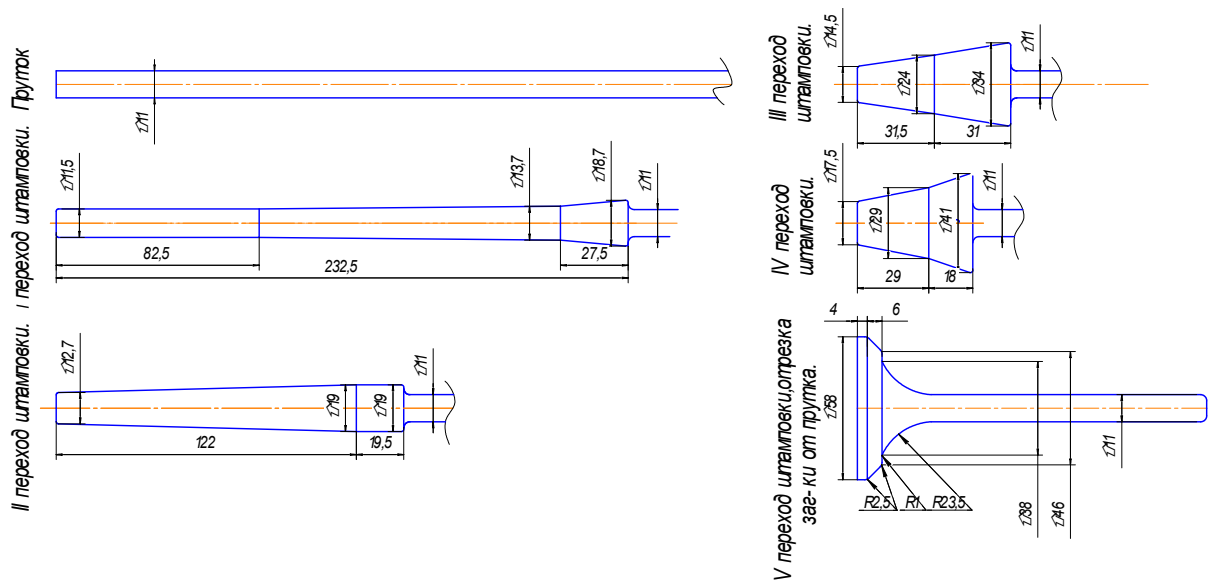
Штамповка заготовки на ГКМ за пять переходов, с последующей отрезкой заготовки от прутка
